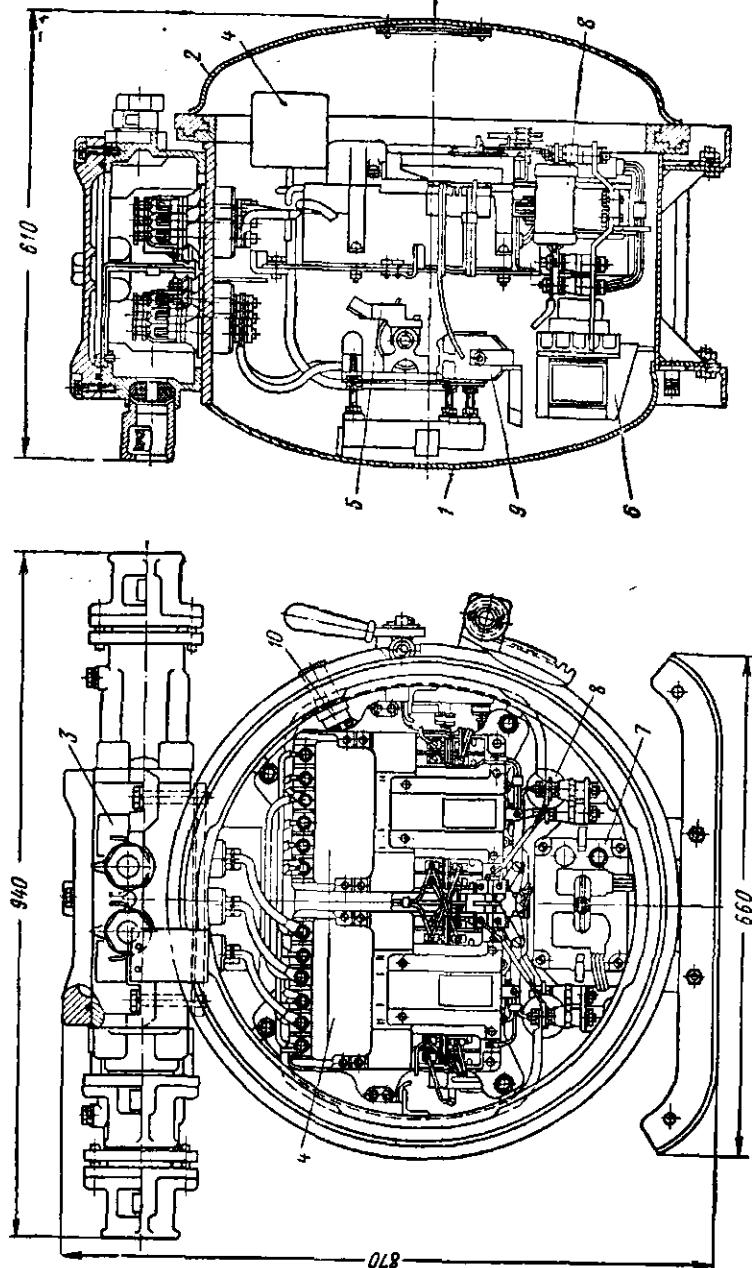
Резорсивный магнитный пускатель ПМЗИР-51
